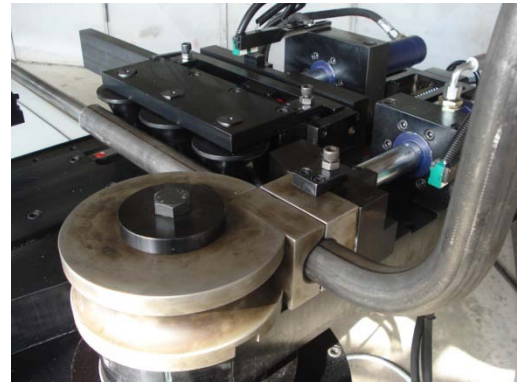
CNC boru bükme makinesi (www.ozismakina.com.tr)
